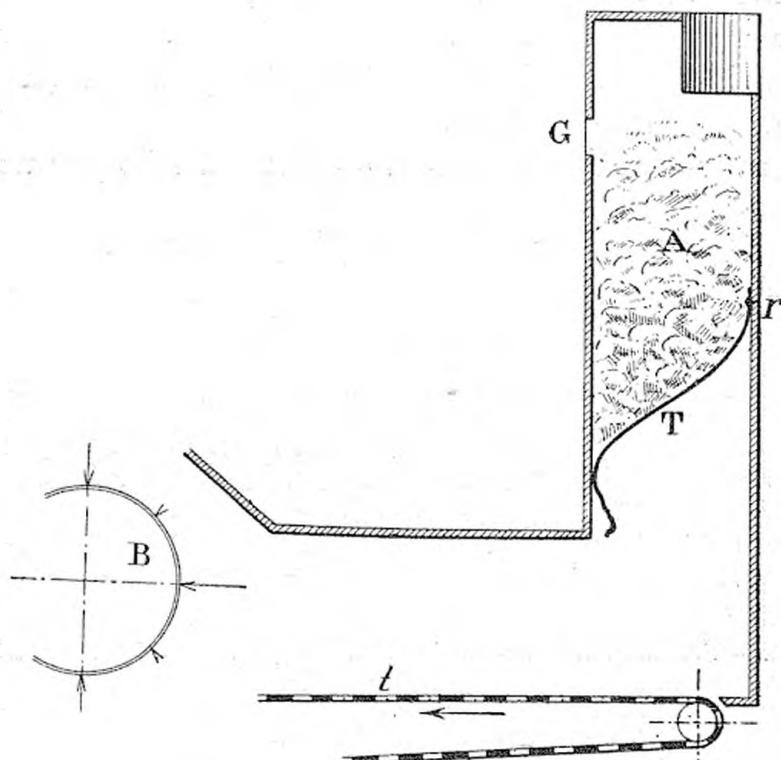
Coupe du conduit, ou caisse d'alimentation.
